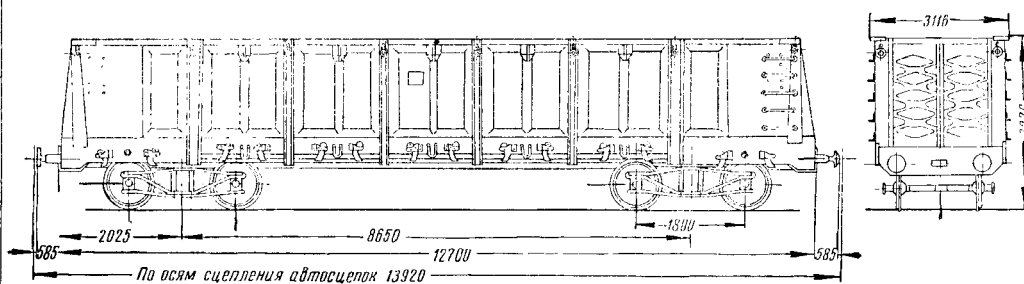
Четырёхосный крытый вагон сварной конструкции грузоподъемностью 50 т
